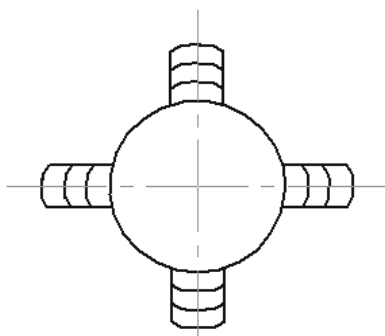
Закріплення заготовки в чотирьохкулачковому патроні
